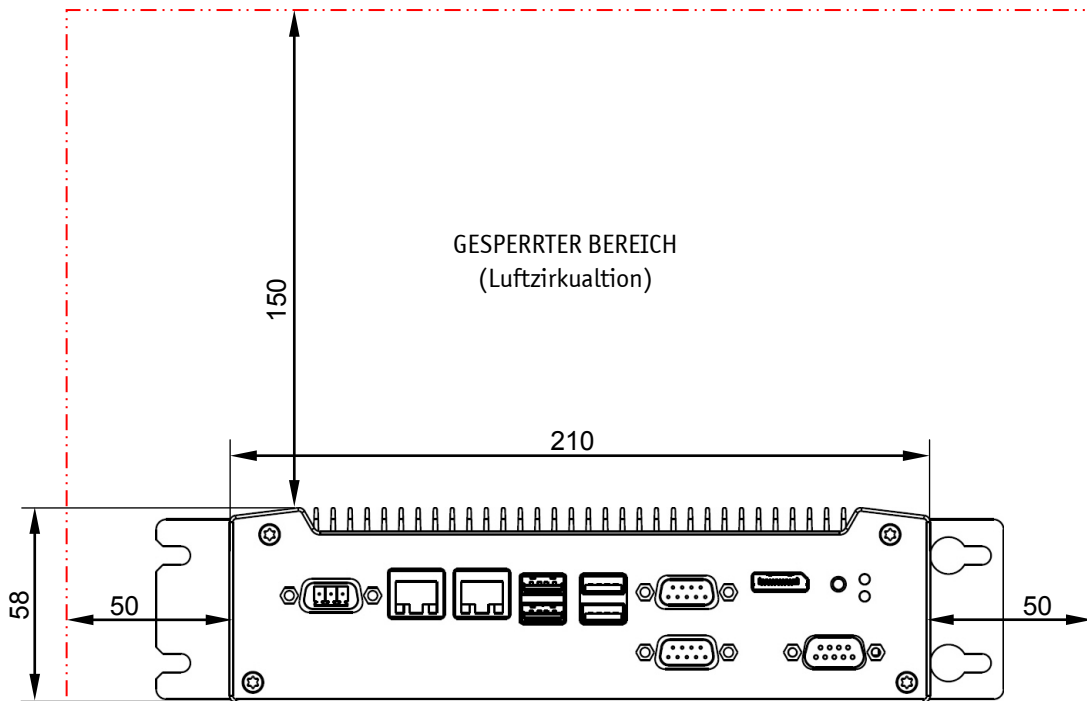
Maßangaben in der Frontansicht (Gehäusemontage)
